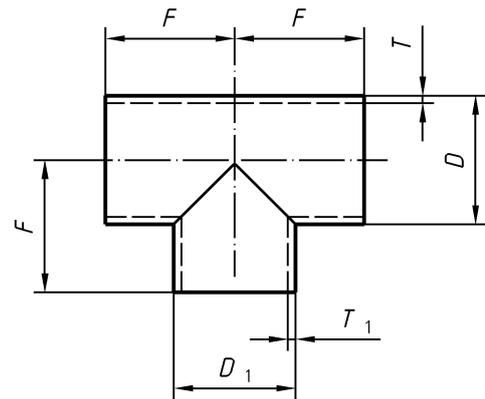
T-Stücke, am Abzweig geschweißt
